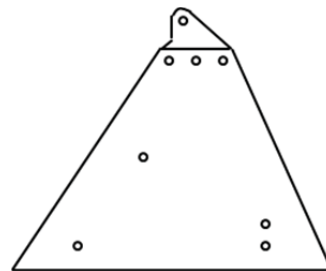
Beispielhaftes Attachment beim Projektpartner.
